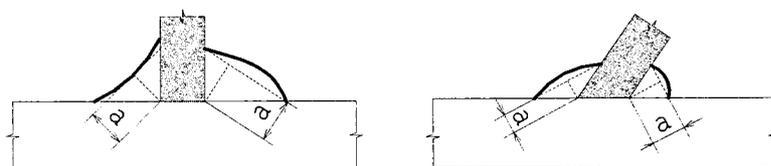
Cordoni d'angolo – Determinazione dell'altezza di gola
